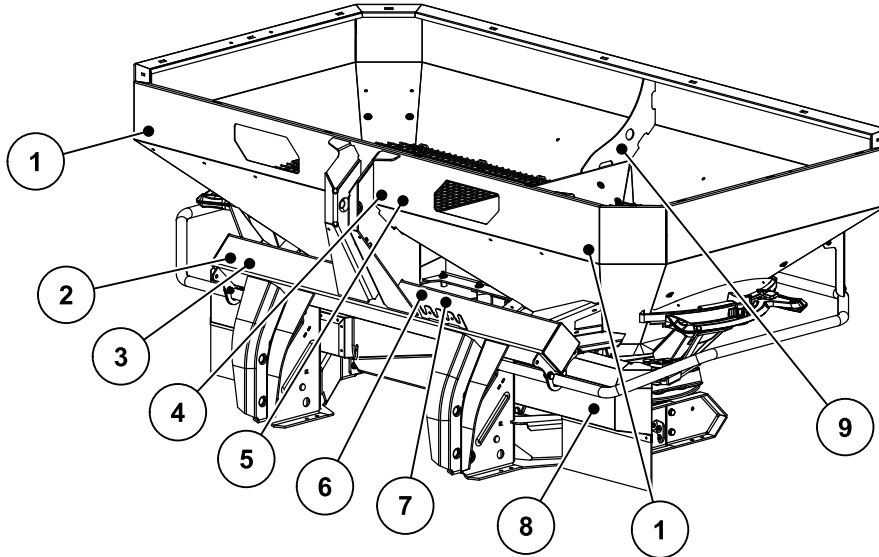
Расположение защитных приспособлений, предупреждений и указаний и рефлектора
